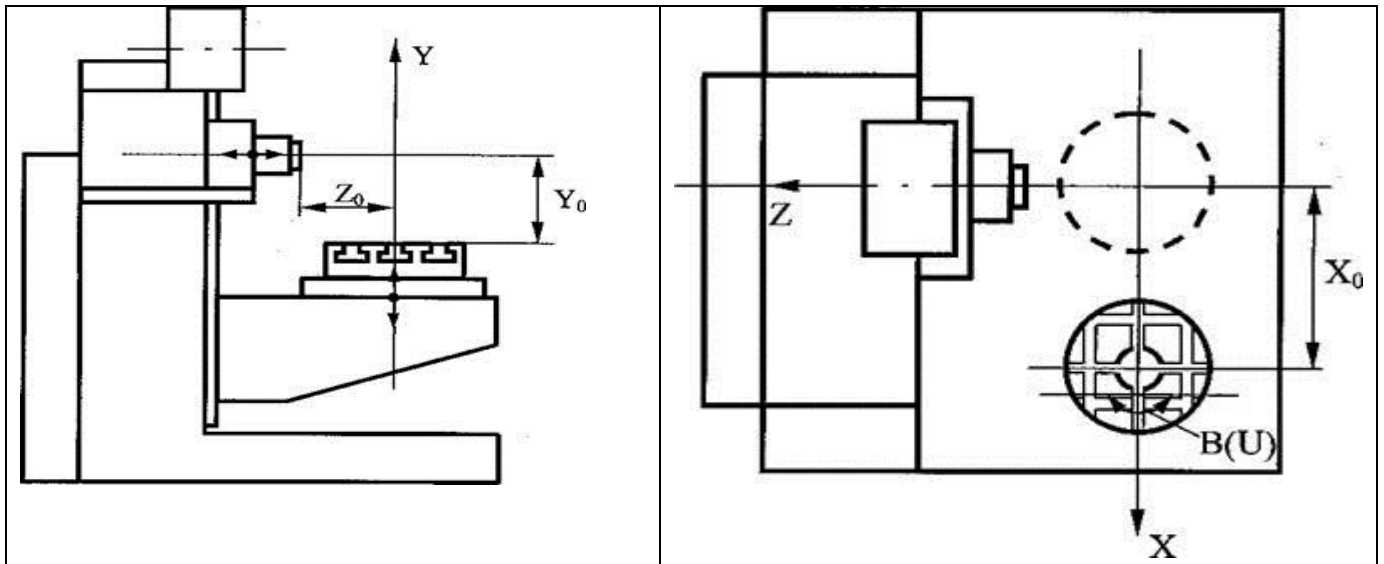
Система координат многоцелевого станка VM501ПМФ4
